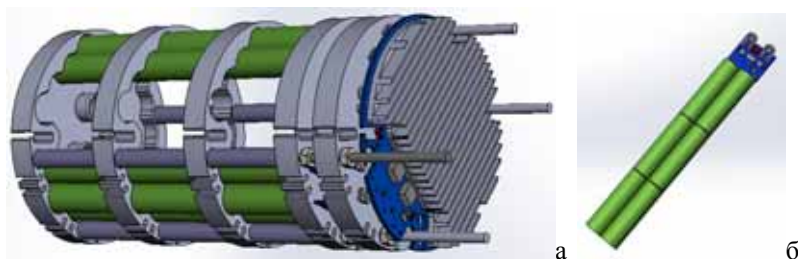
Общий вид блока питания из 16 сборок аккумуляторов Panasonic NCR18650PF с общей платой управления (а); общий вид сборки из 6 аккумуляторов с платой контроля и защиты (б)
